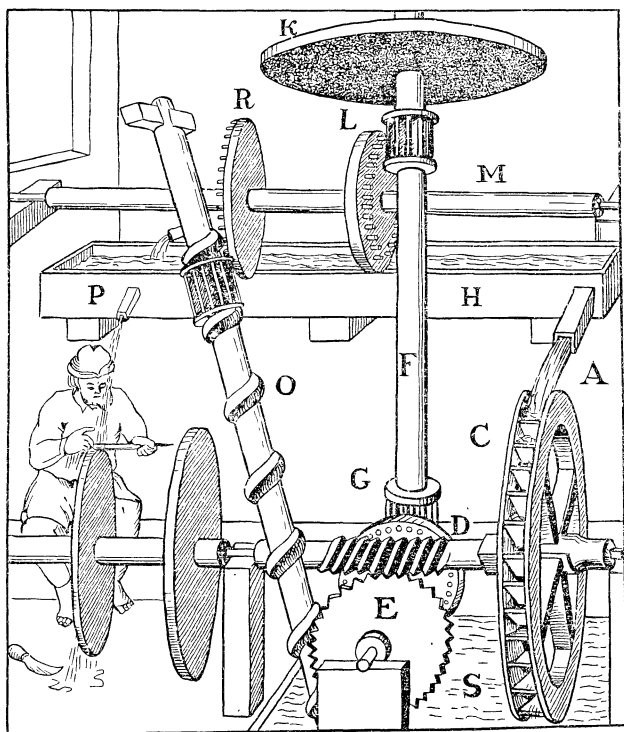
Гидравлический двигатель для привода точильного камня
